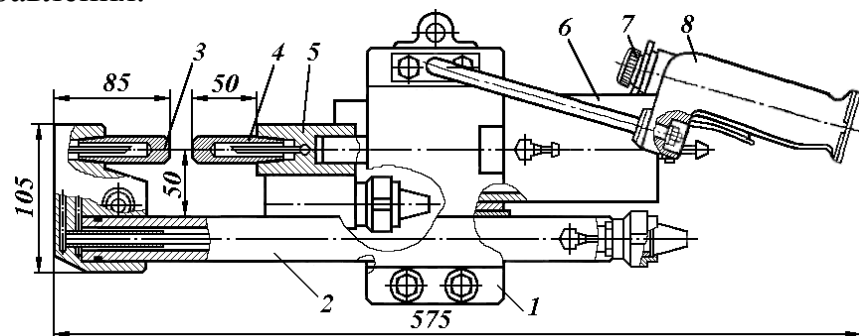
Сварочные клещи КТП-8-2
